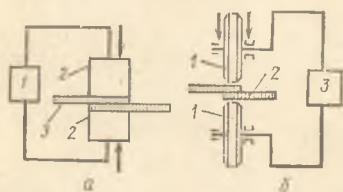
Схема сварки токами высокой частоты
